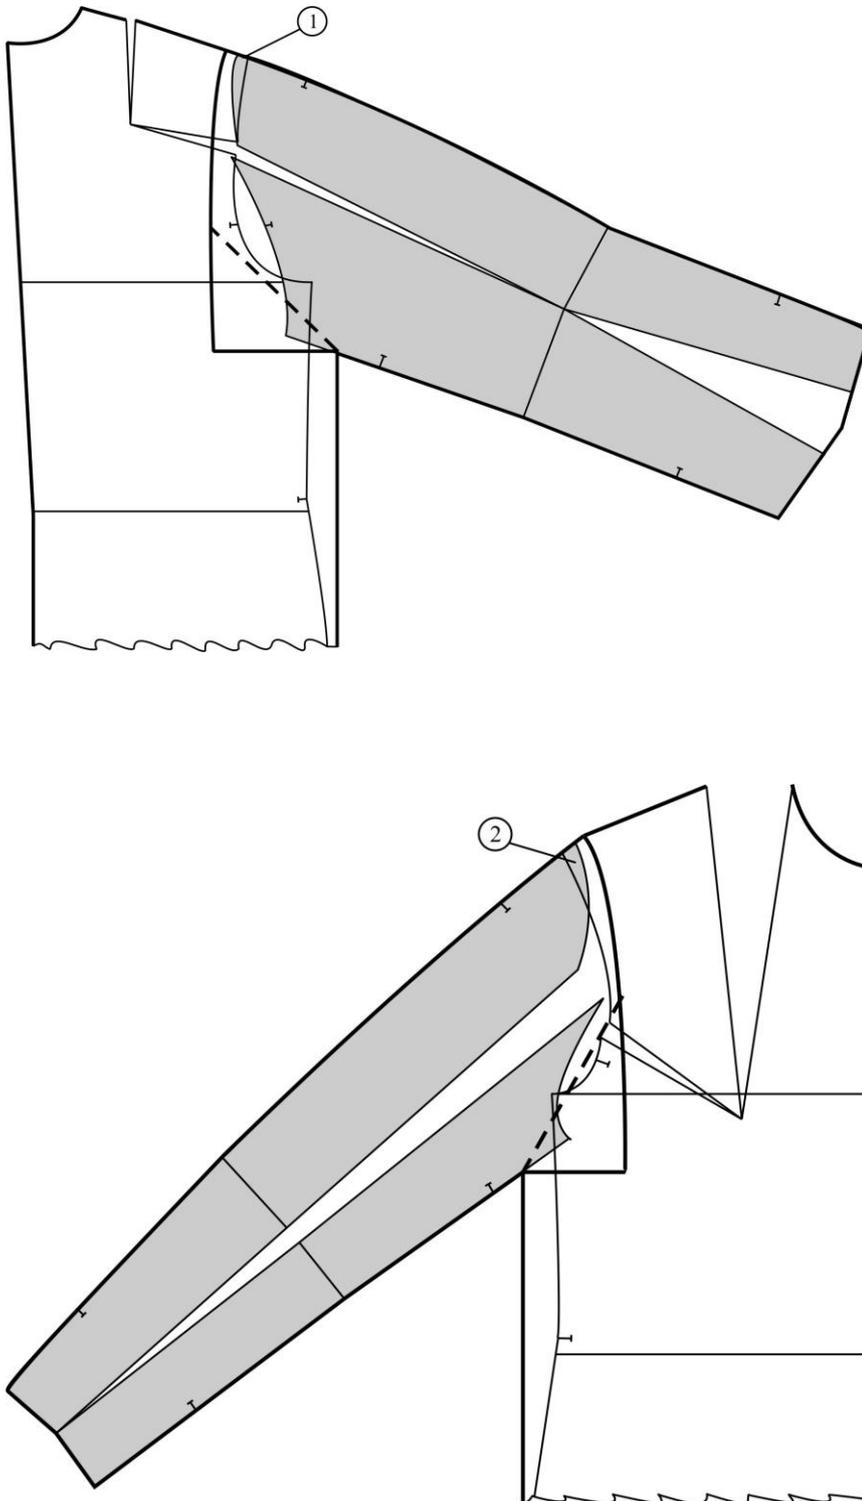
Совмещение деталей переда и спинки с деталями рукава
